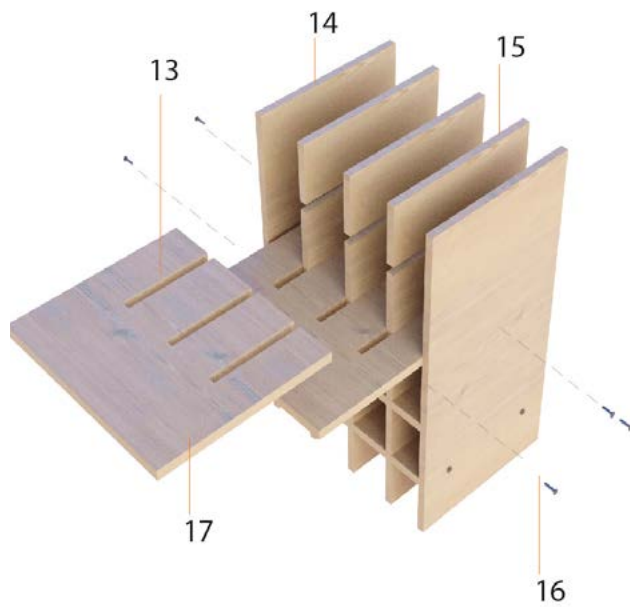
Detalle constructivo 3d vinera con madera de pino
